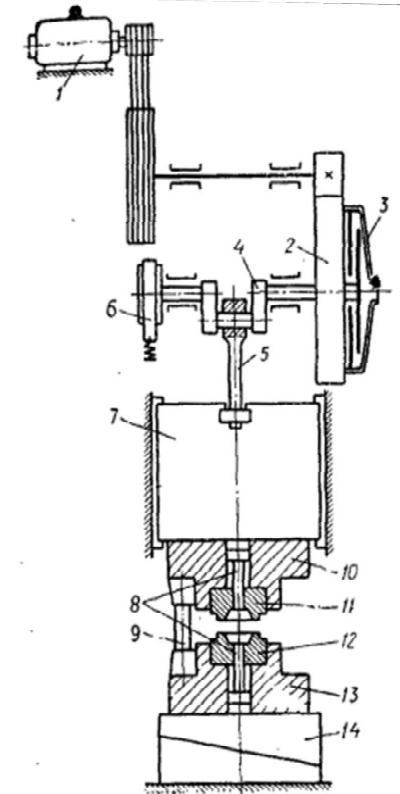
Схема кривошипного гарячоштампувального преса:
